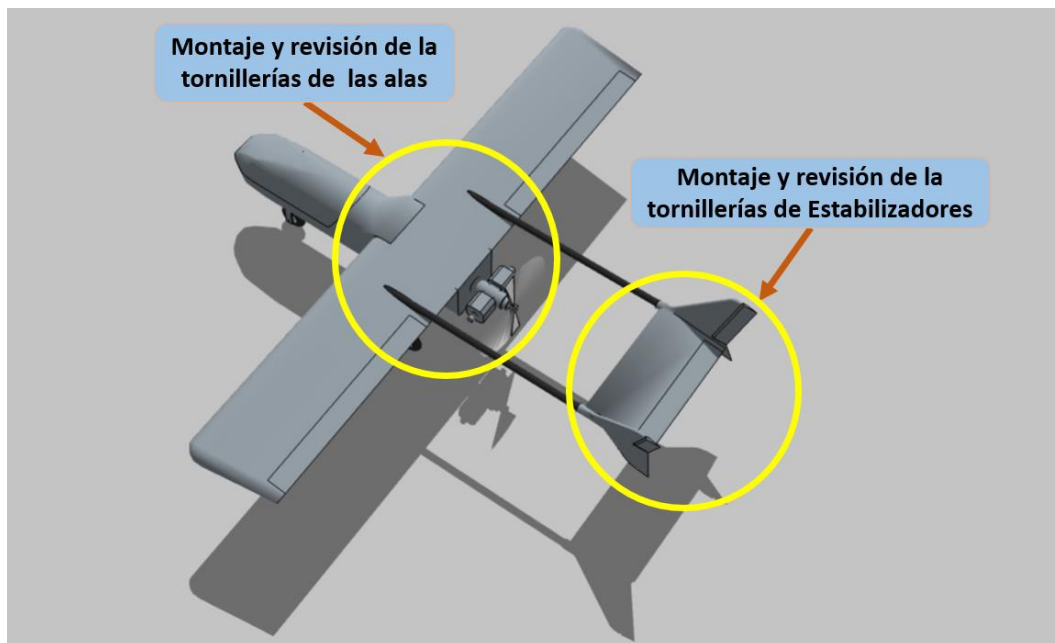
Esquema del montaje y revisión de la tornillería del UAV.
